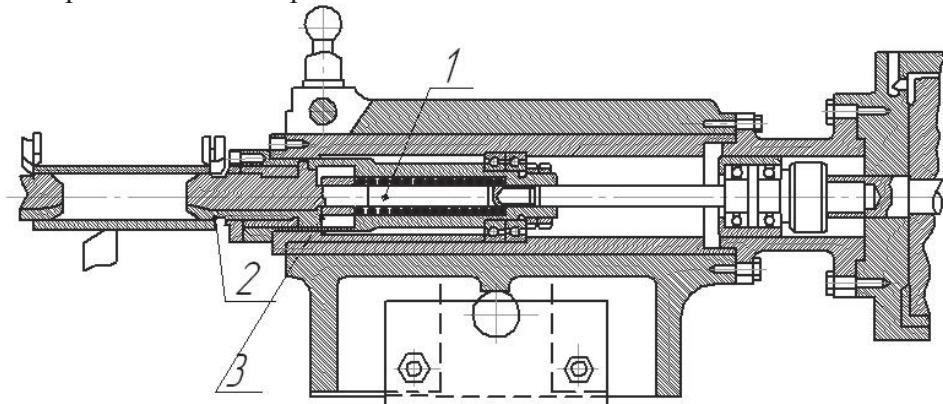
Автоматичні лещати з пневматичними установками, установлені на супорті верстата для одночасної обробки торців гильзи циліндрів двигуна
